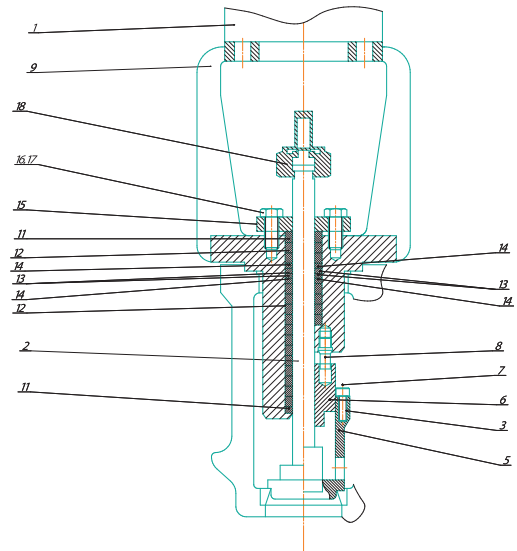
Регулирующий клапан SIEMENS. Установка пиролиза
